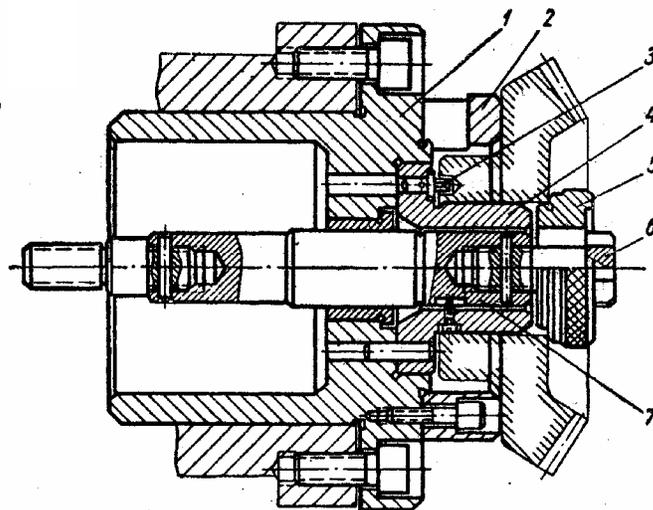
Оправка для обработки конического зубчатого колеса
